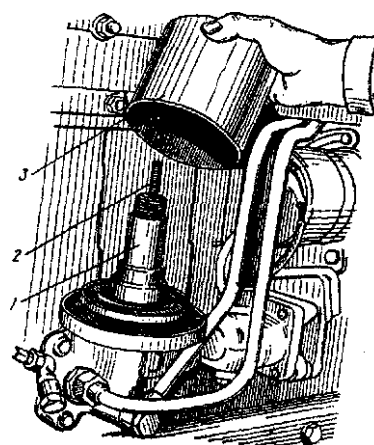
Зняття стакана відцентрового оливоочисника: 1 - корпус ротора; 2 - вісь ротора; 3 - стакан ротора.
